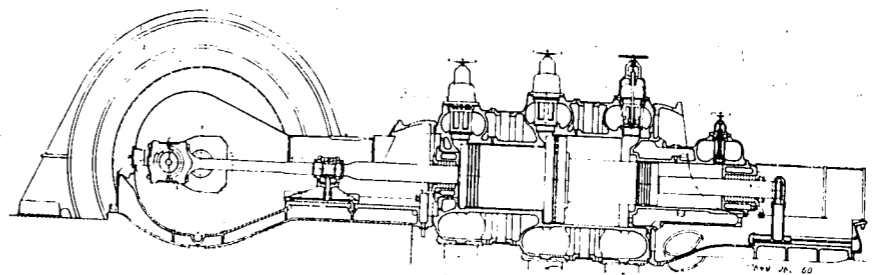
Dreistufiger Koksofengaskompressor, geliefert für ein Stickstoffwerk, gekuppelt mit Drehstrommotor, Ansaugmenge std. 5300 m³, Druck 13 atü, Drehzahl min: 122 (s. Abb. 23)
